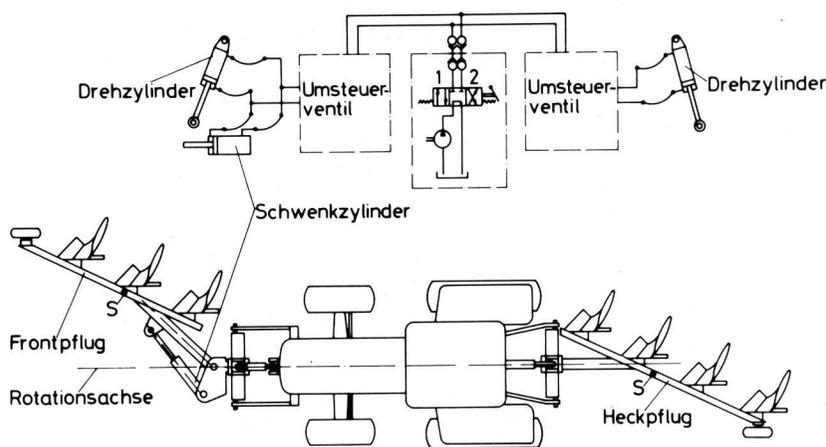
Hydraulische Betätigung zweier druckabhängig umgesteuerter Doppelhub-Drehwerke an Front- und Heckpflug [5].
